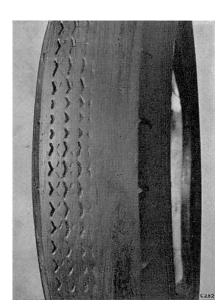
Usure d'un pneu causée par un carrossage excessif de la roue avant
